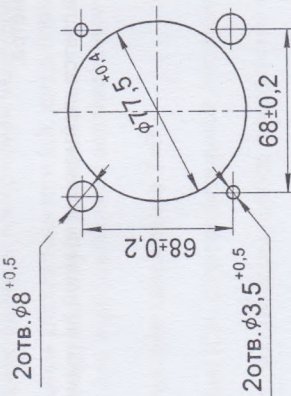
Разметка отверстий в щите (вид спереди) для крепления омметра
